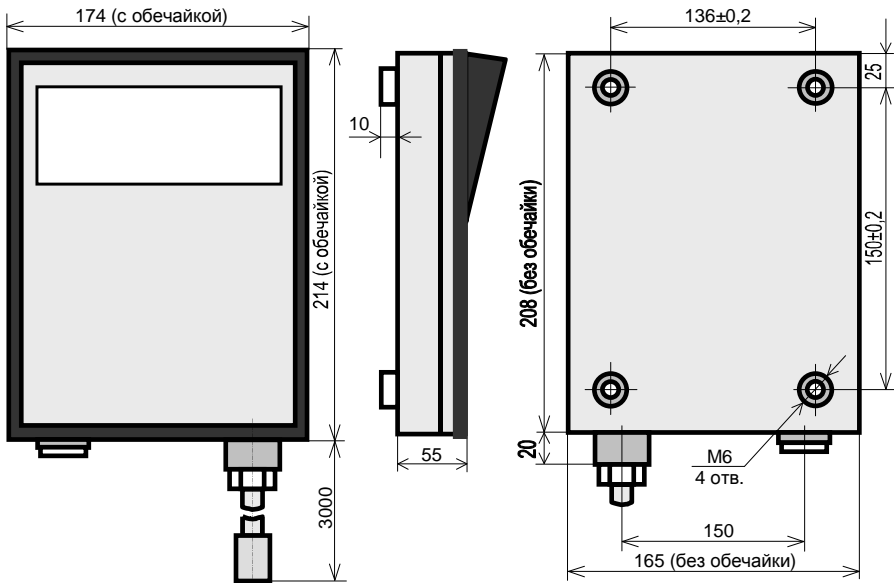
Габаритные и присоединительные размеры БОИ
